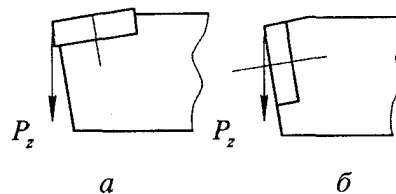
Способи розташування пластини: а - радіально; б – тангенціально
